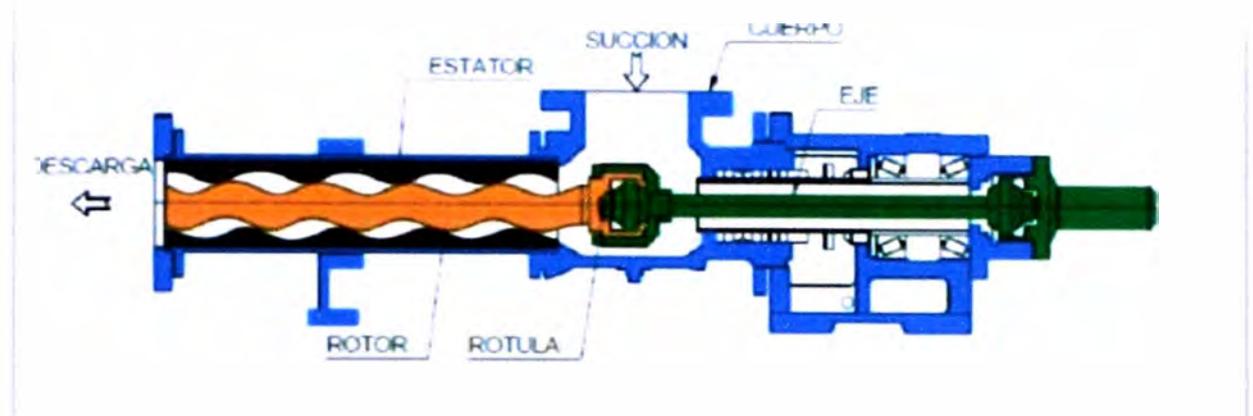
Partes de bomba de cavidad Positiva MOYNO
